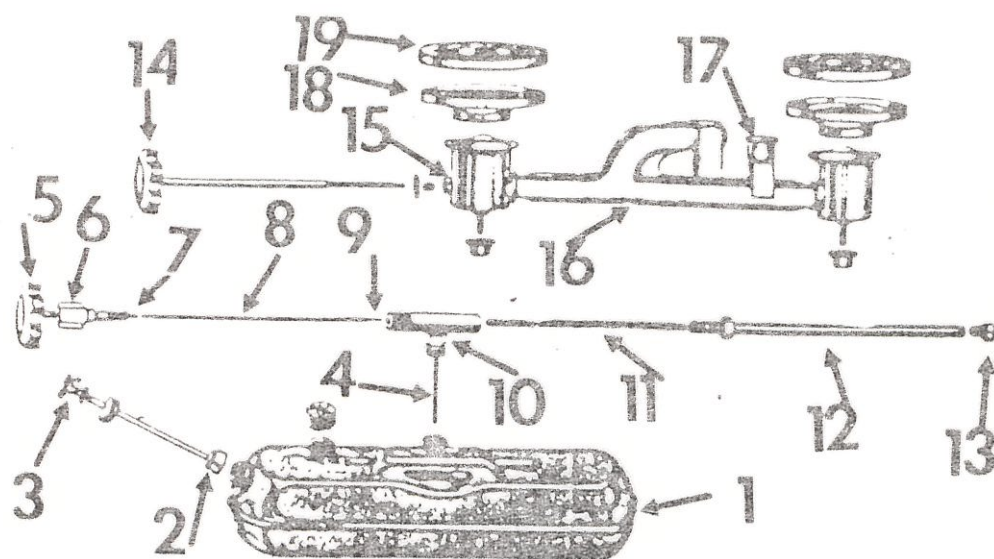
DESPIECE DEL SISTEMA DE COMBUSTION Y EL TANQUE EN LA COCINA SUPERIOR DE PRESION
